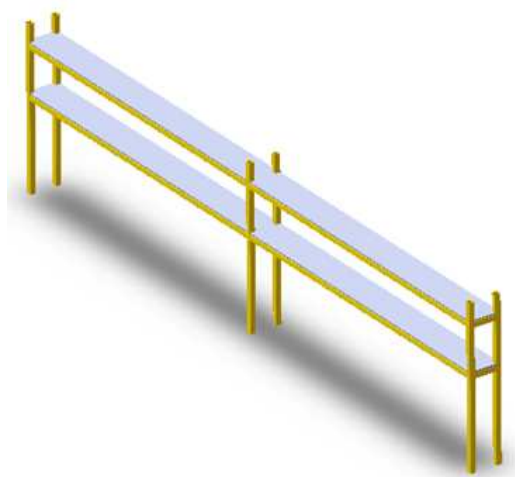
a: Estantería para ubicar tubería y acero estructural
